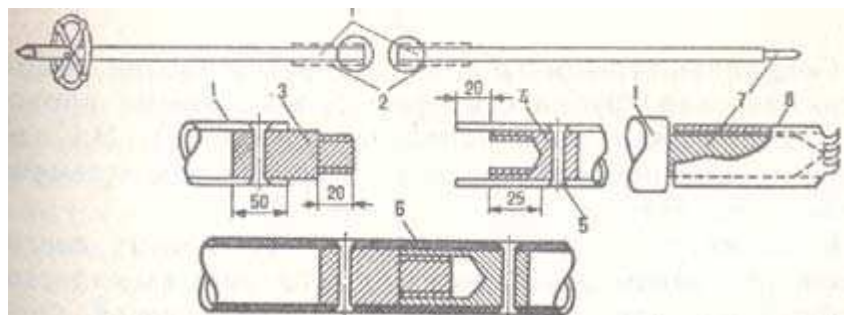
Лавинный щуп из лыжных палок: 1 — лыжные палки; 2 — снимаемые рукоятки; 3 — болт; 4 — втулка; 5 — заклепка; 6 — соединенные палки; 7 — штычок; 8 — насадка.
